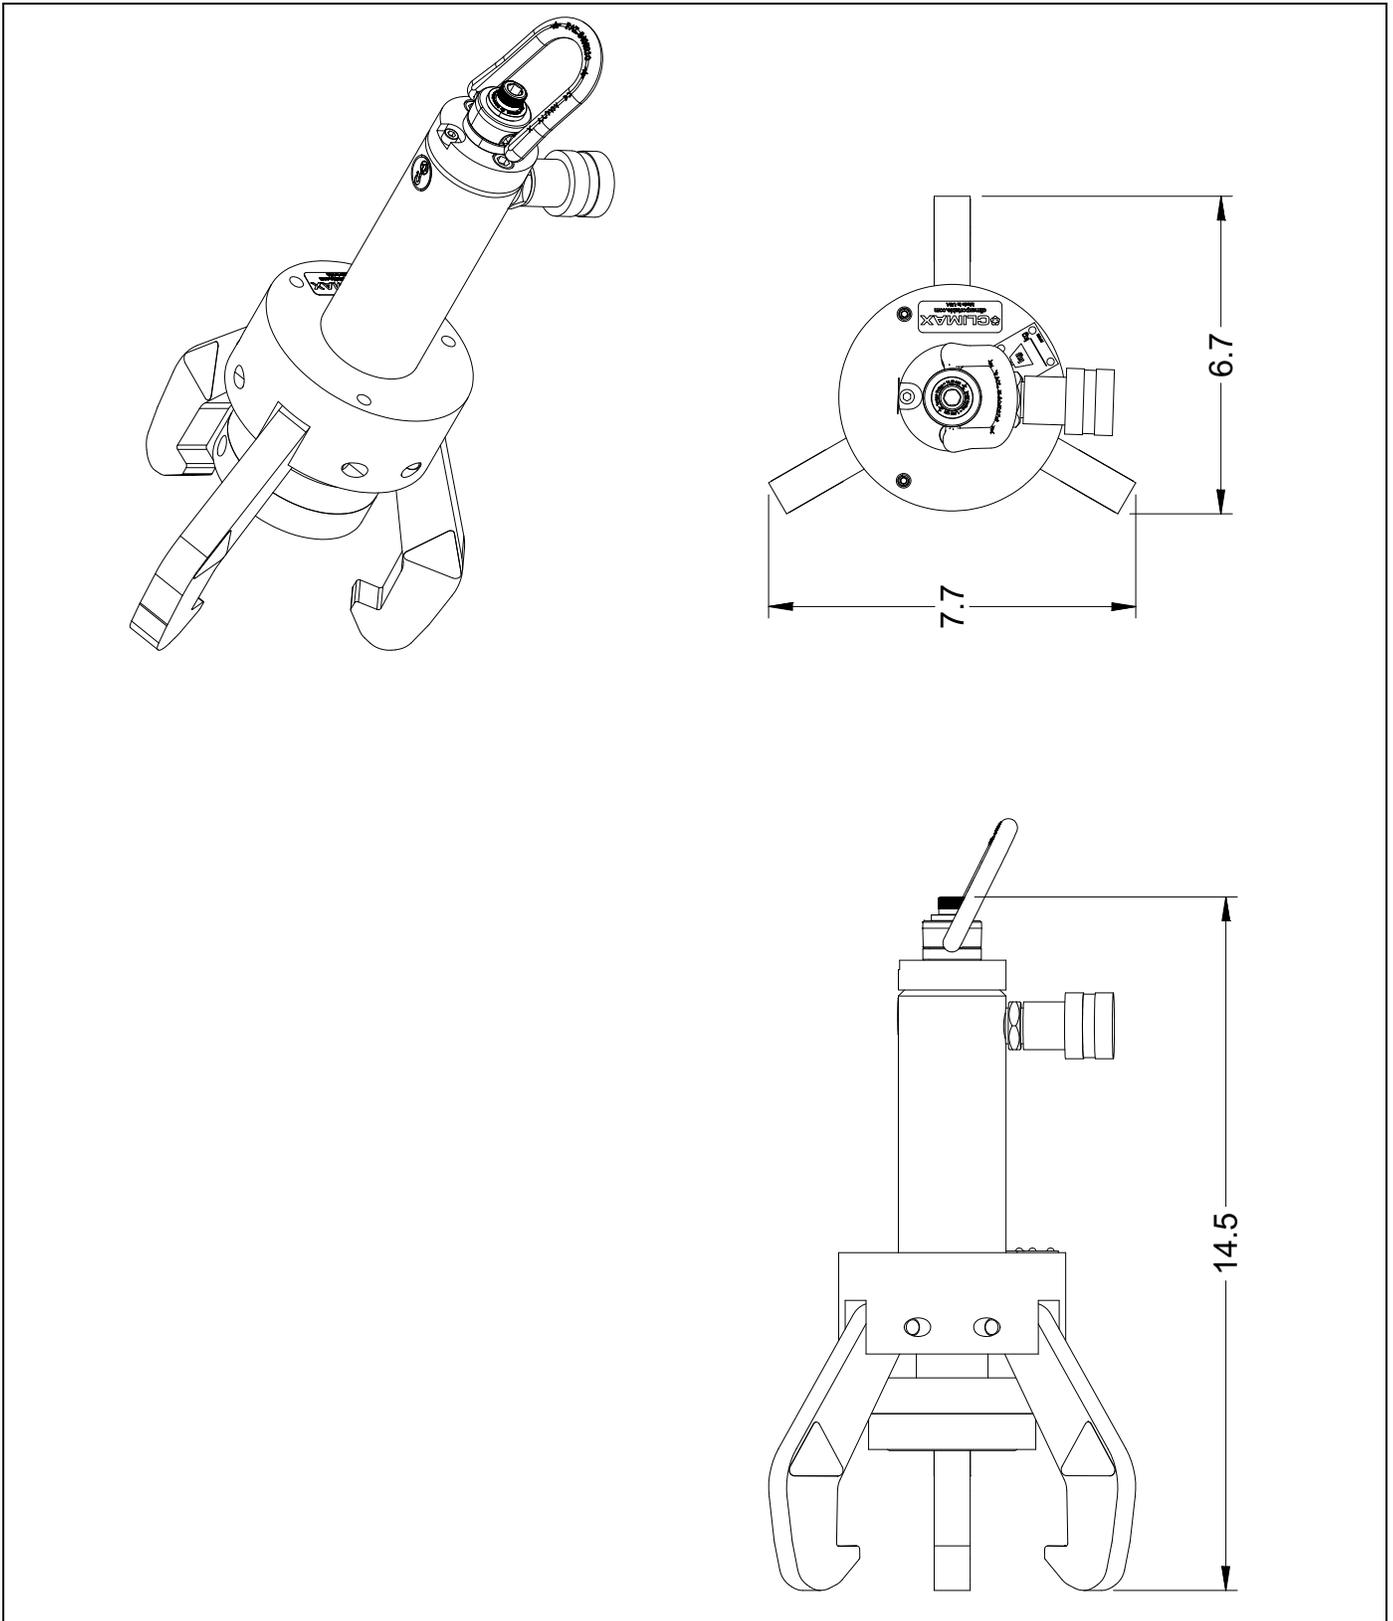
DIMENSIONS DE LA HFS-2
